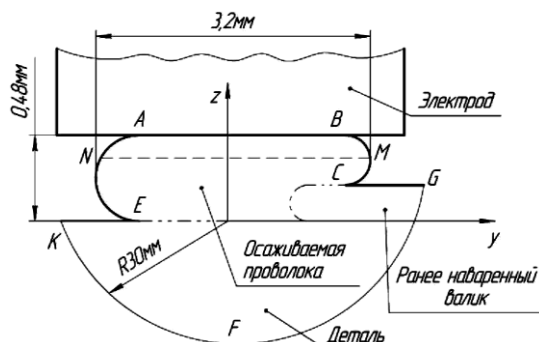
Расчетная схема определения ширины сварочного ролика при электроконтактной наплавке
